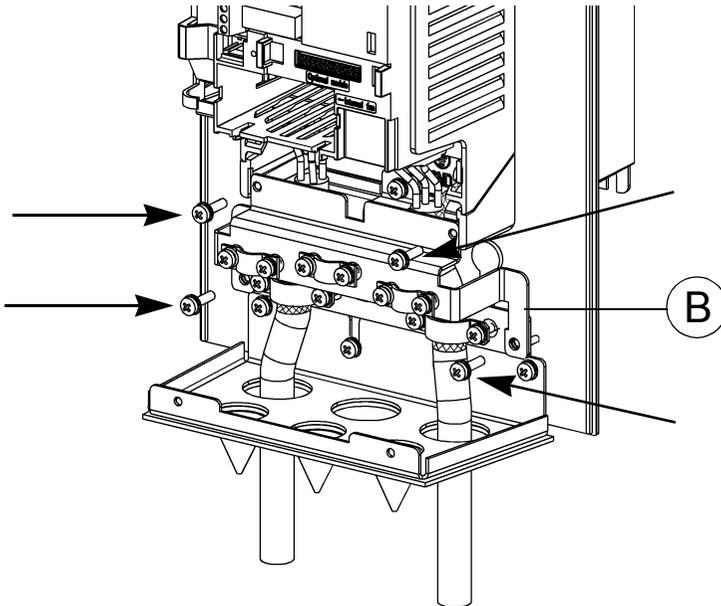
Durchführungsblech für Steuerkabel (B) montieren; Frequenzumrichter des Typs IP 54 / NEMA12.
